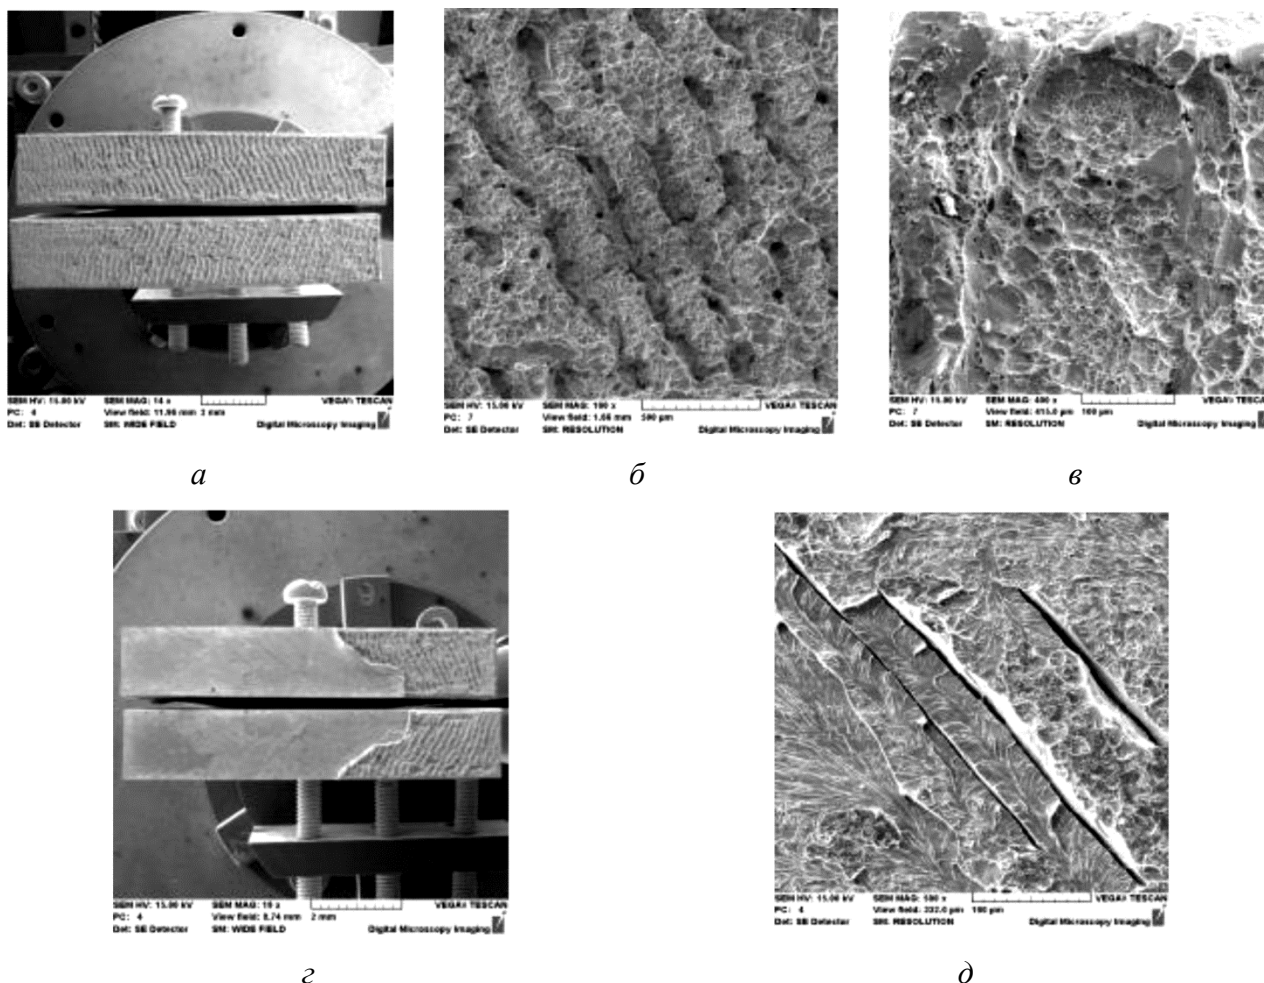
Макро- (*а, з*) и микрорельеф (*б, в, д*) поверхности разрушения образцов сварного соединения с композитной вставкой; разрушение по границе с медной пластиной (*а, б, в*); хрупкое разрушение по границе Nb/Ti (*з, д*) [33]
